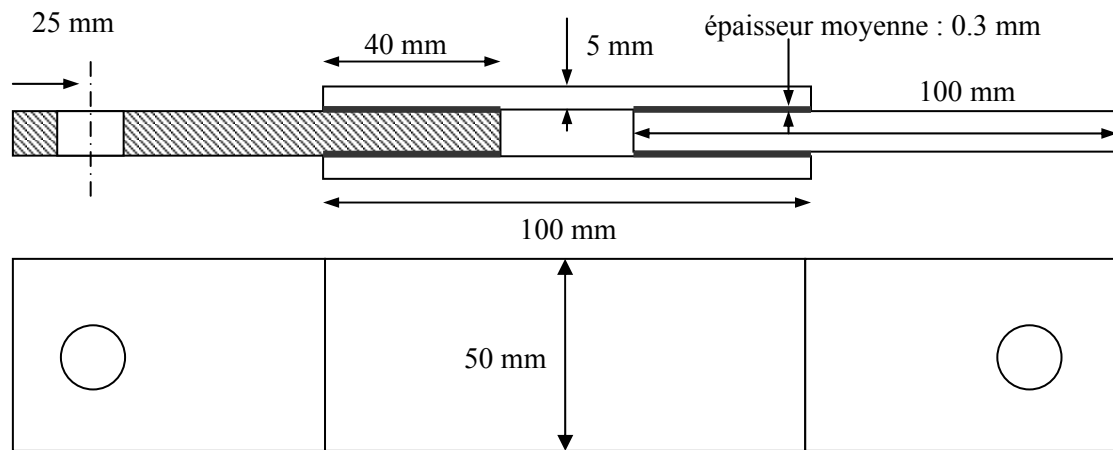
Géométrie des éprouvettes de quadruple cisaillement
